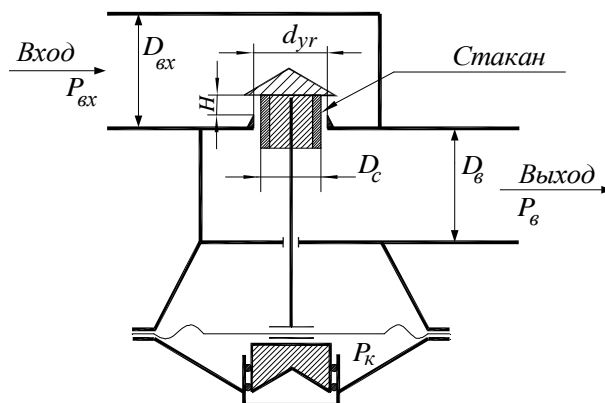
Усовершенствованный стандартный редуктор со «стаканом»
